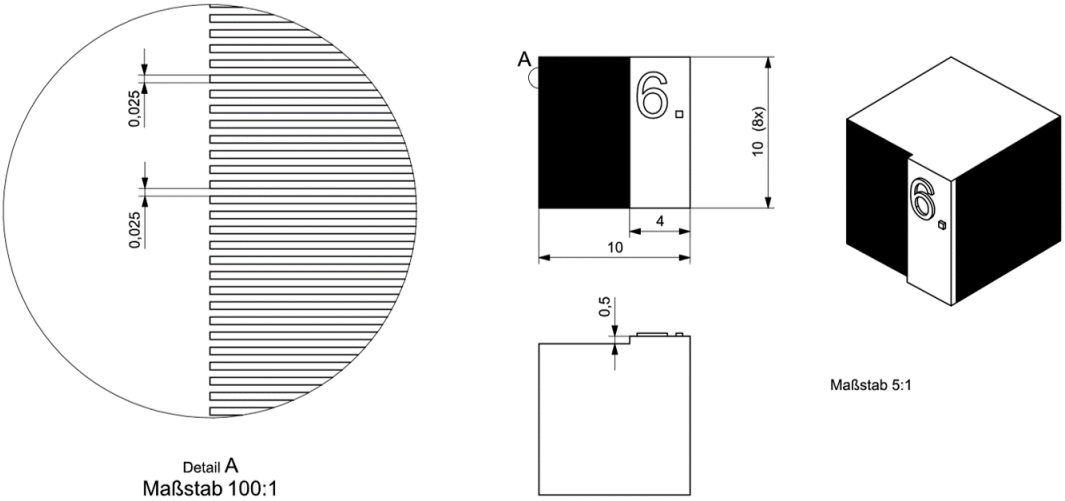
Technische Zeichnung der Dichtewürfel mit einer Schichtdicke von 50 μm
